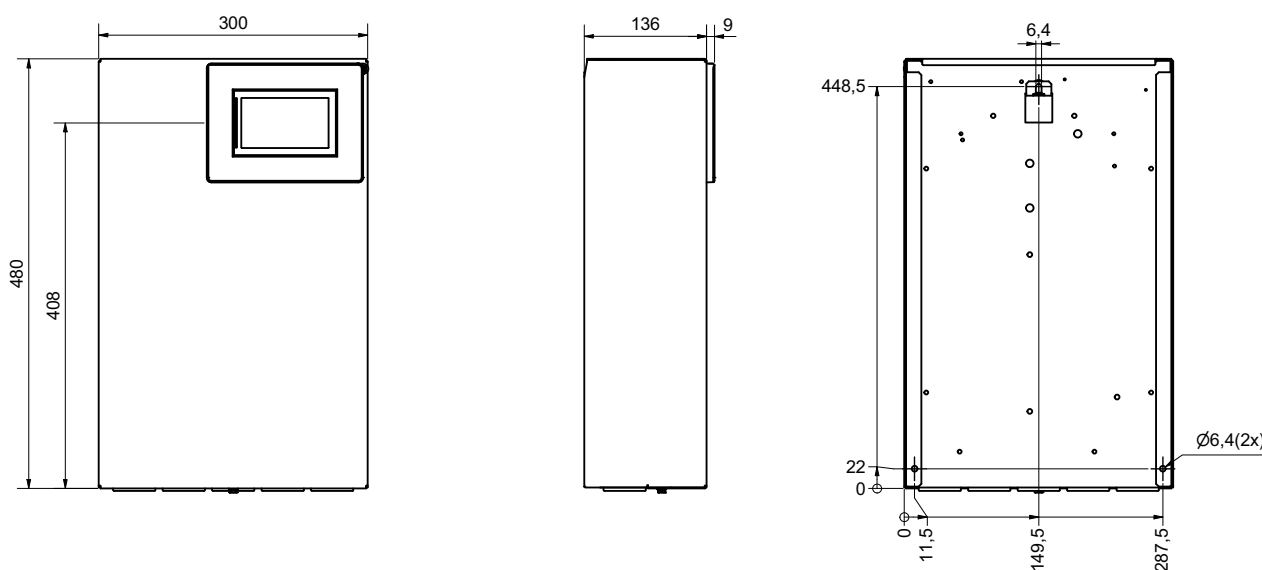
Dimensioni del regolatore master per riscaldamento montato a parete
